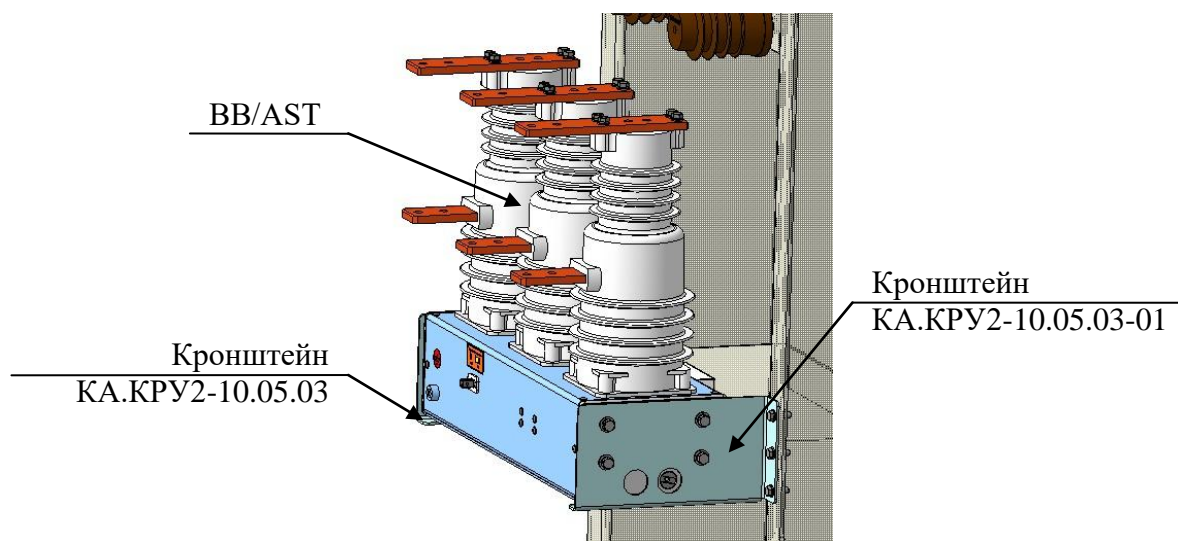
Установка ВВ/АСТ и его кронштейнов навески
